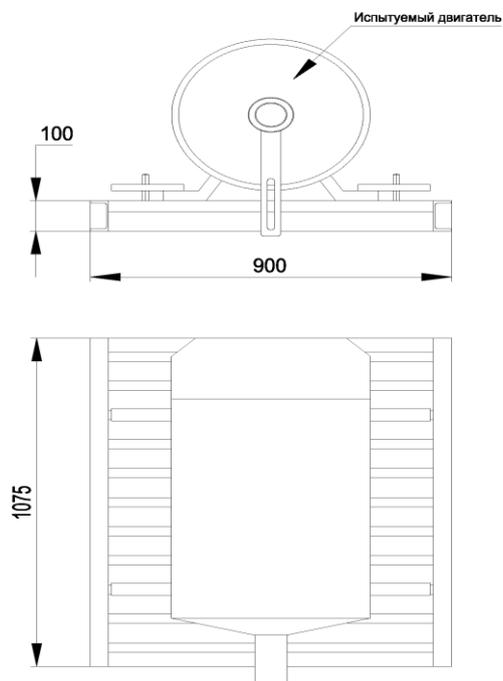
Габаритный чертеж испытательной платформы КСПАД – 006.
